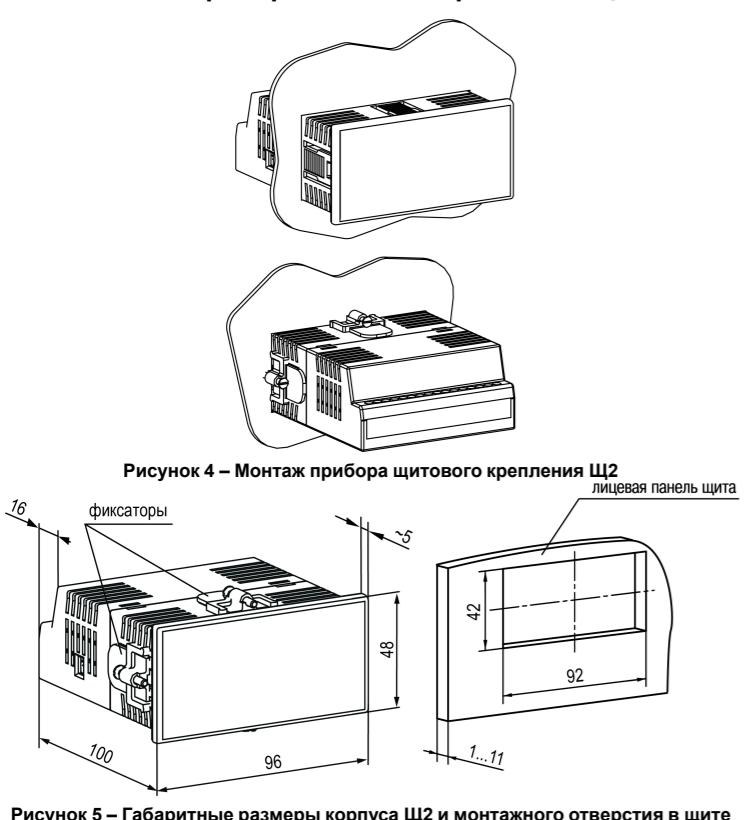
Монтаж прибора щитового крепления Щ2
